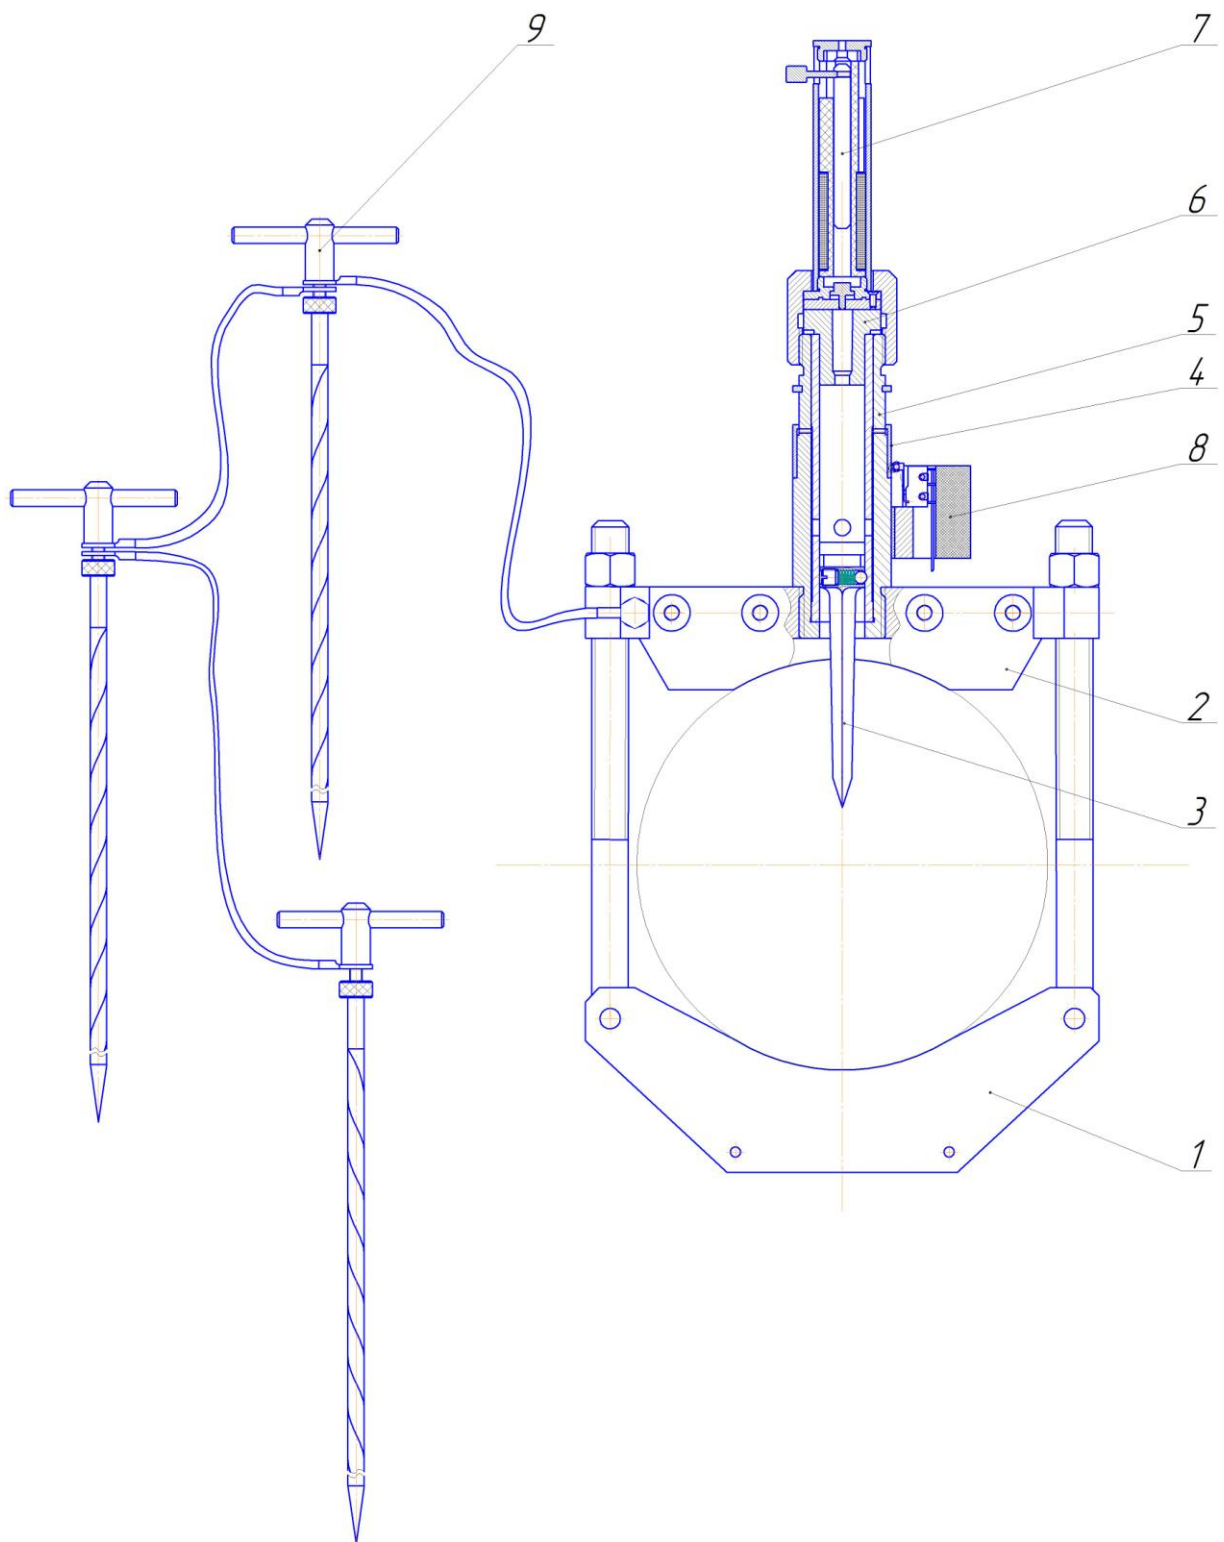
Силовая часть устройства прокола кабеля УПКП 220
